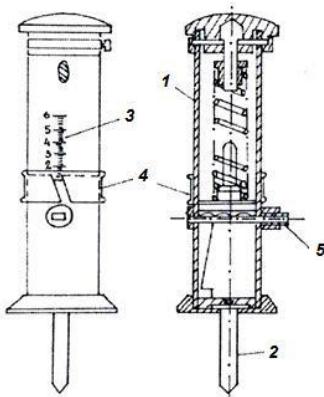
Твердомір конструкції Н.А. Качинського: 1 – корпус; 2 – плунжер; 3 – шкала; 4 – рухоме кільце (показчик); 5 – фіксатор
